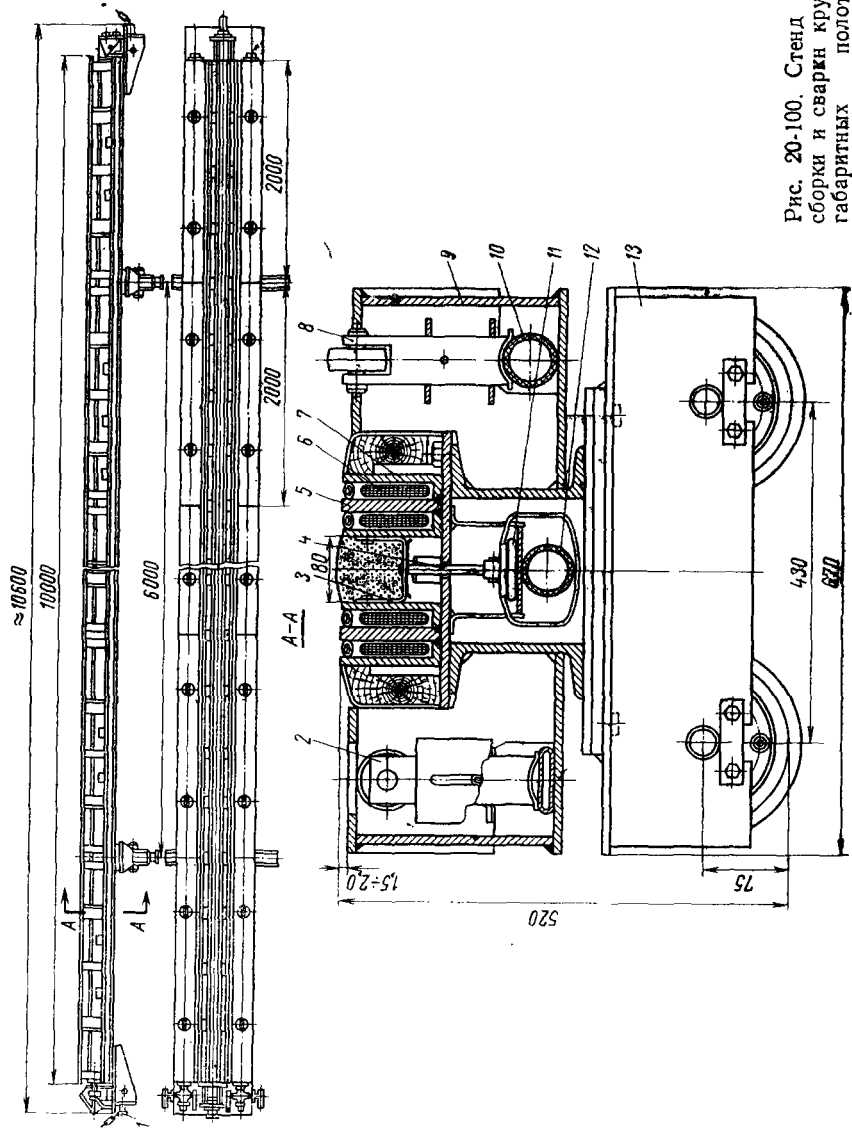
Стенд для сборки и сварки крупногабаритных полотен
